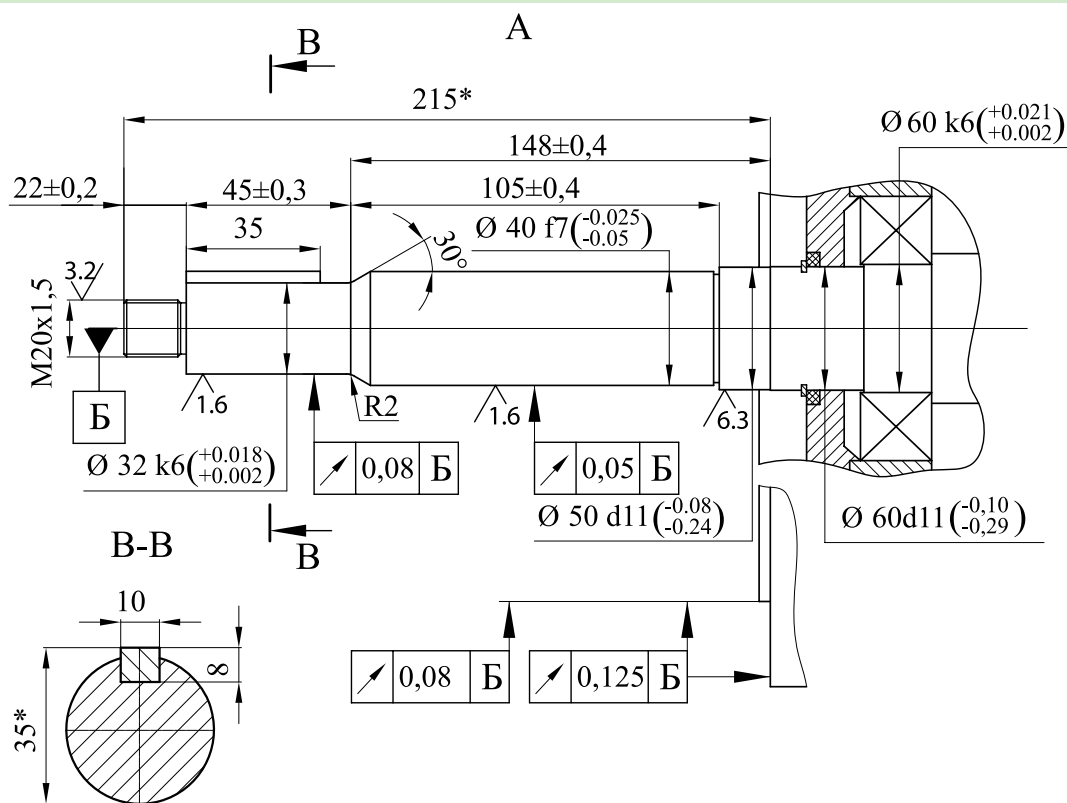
Свободный конец вала двигателя 6АМУ180М2ЖУ2
